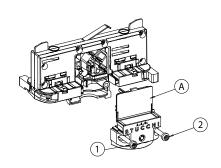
Chiusura dell'adattatore Pic. 2 Adapter closure
